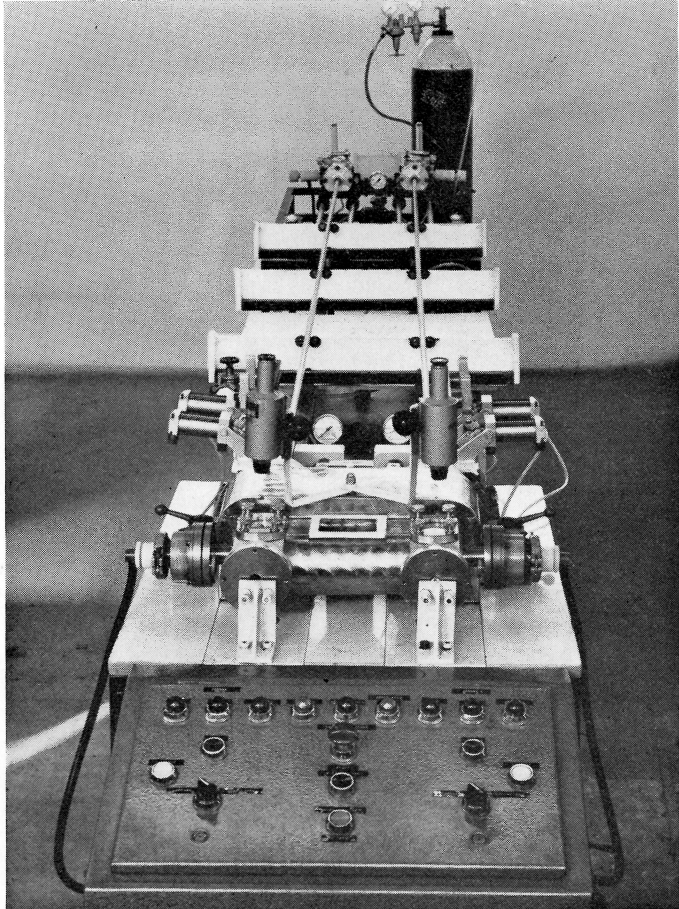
Schweißmaschine für Hüllrohre. Die dargestellte Maschine wird für die Anfertigung der 1. Schweißnaht eingesetzt. Im Vordergrund hinter dem Bedienungspult zwei Schweißkammern, in die zwei Hüllrohre über eine Vakuumdichtung eingeführt sind. In der Kammer befindet sich hochreines Argon (Flasche im Hintergrund). Durch zwei Fenster läßt sich mit je einem Mikroskop die Einstellung der Elektroden kontrollieren.
